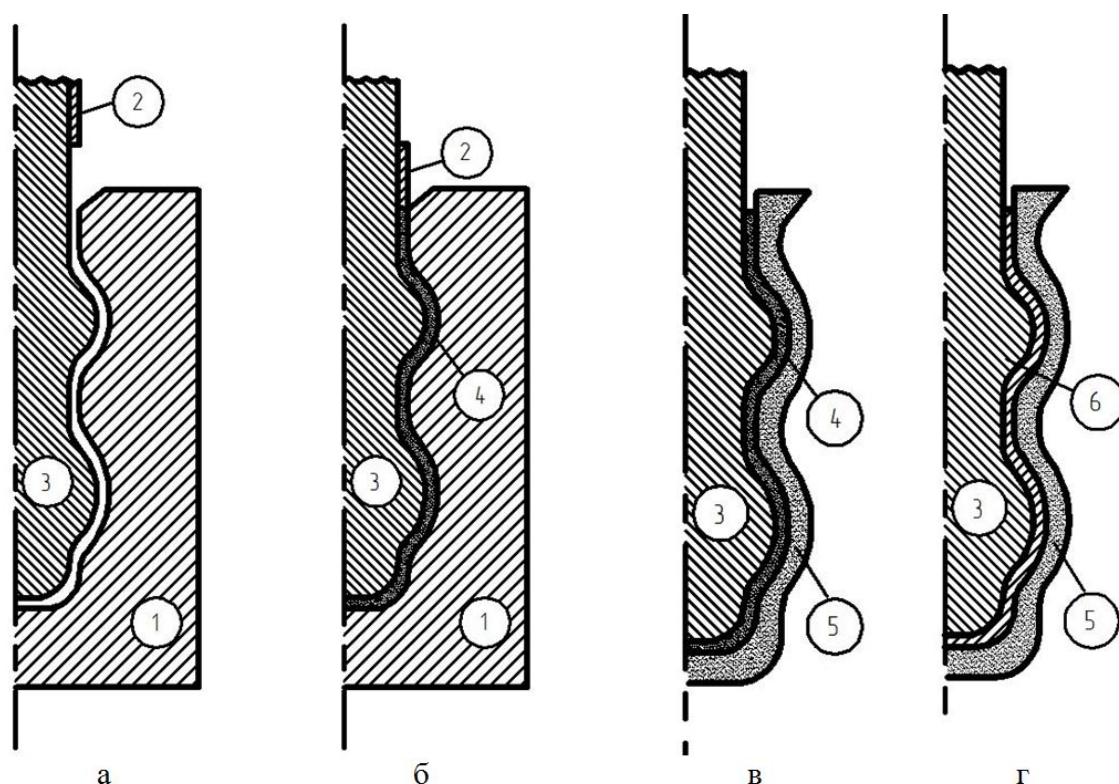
Схема последовательности формирования биметаллической отливки: 1 – пресс-форма; 2 – подвижный пресс-пуансон; 3 – стальной каркас; 4 – воскообразный напрессованный слой; 5 – керамическая оболочка; 6 – биметаллическая отливка в оболочковой форме.
